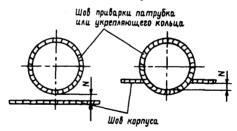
Схема определения расстояния между краем шва корпуса и краем шва приварки детали
